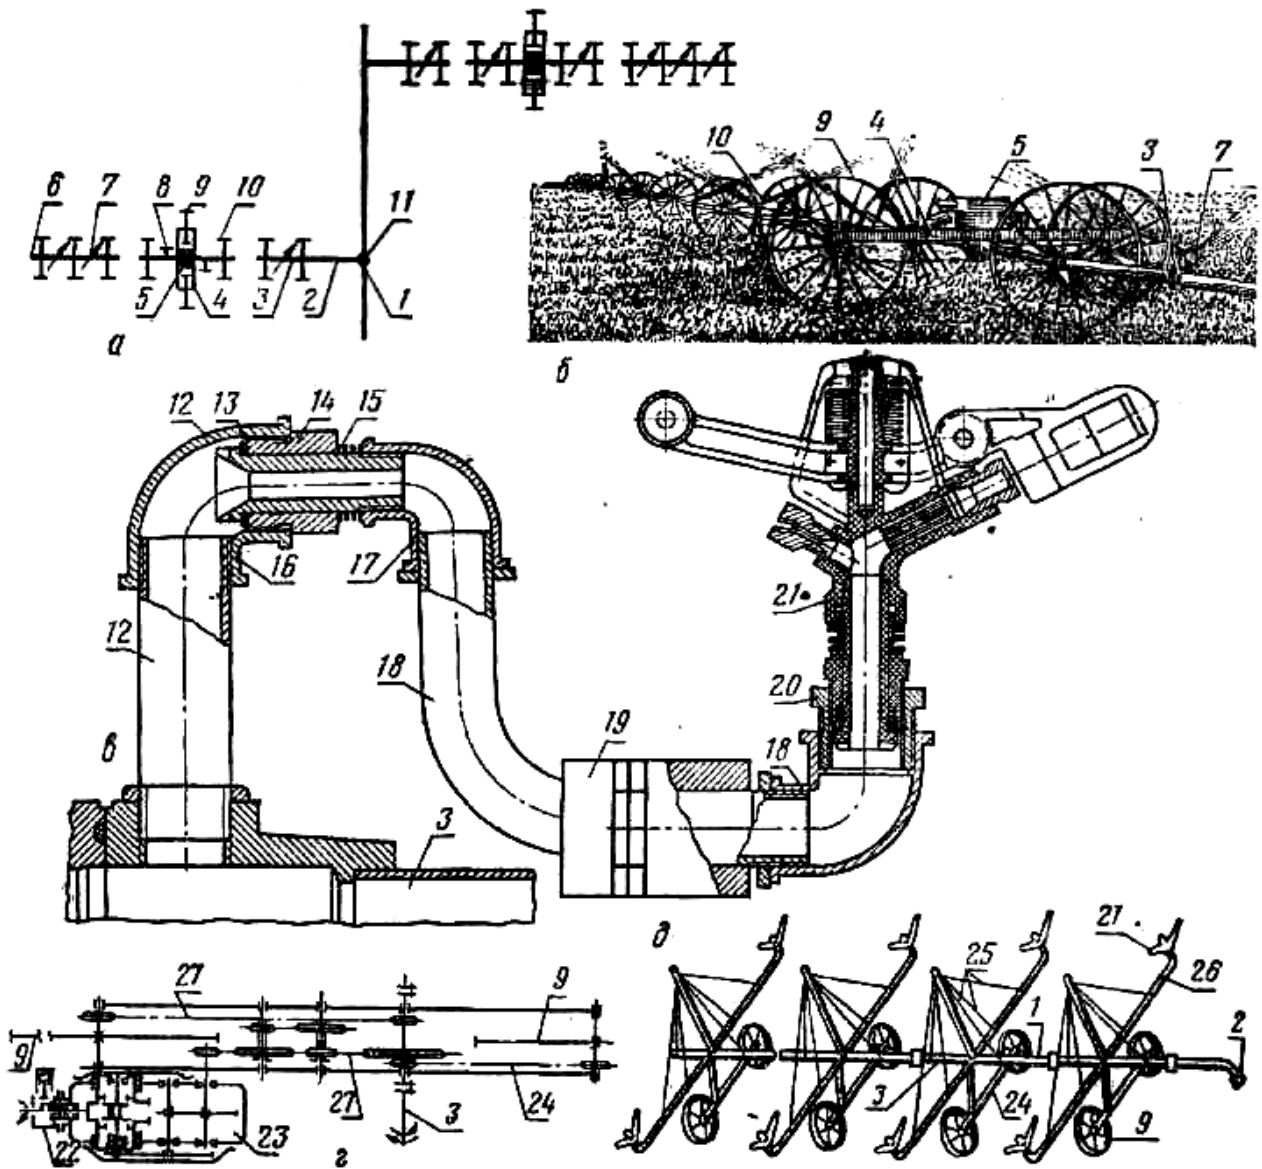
Самоходные многоопорные дождевальные машины фронтального действия: с двигателем внутреннего сгорания: *а* — схема; *б* — общий вид; *в* — механизм самоустановки дождевального аппарата; *г* — кинематическая схема приводной тележки; *д* — с электроприводом (общая схема); 1-оросительный трубопровод; 2-узел присоединения; 3 -секция; 4 -приводная тележка; 5-двигатель; 6 -концевая заглушка; 7 -дождевальный аппарат с механизмом самоустановки; 8- тормозной упор; 9 -ведущее колесо; 10 -опорное колесо; 11-гидрант с колонкой; 12-стояк; 13 -уплотнительное кольцо; 14 - гайка; 15-пружина; 16, 17 - угольник; 18 - колено; 19 -противовес; 20 - футорка; 21- дождевальный аппарат ; 22 -двигатель; 23-реверс-редуктор; 24- тележки-опоры; 25 - раскосы и расчалки; 26 -открылки; 27- цепные передачи.
